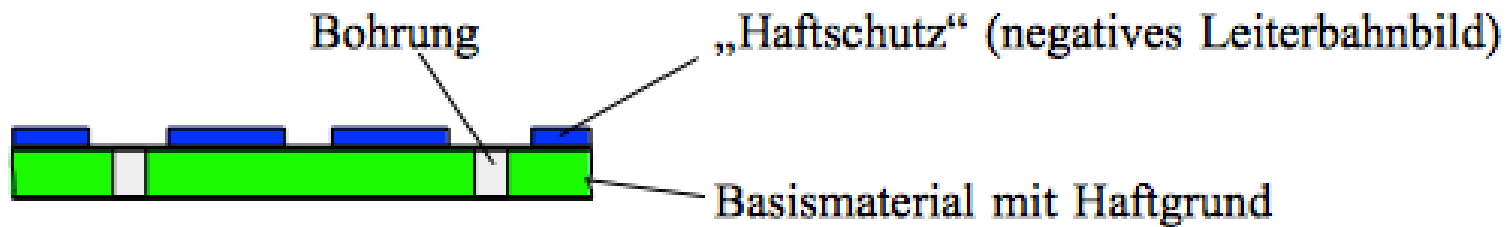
Gebohrtes Basismaterial mit aufgebrachtem „Haftschutz“
